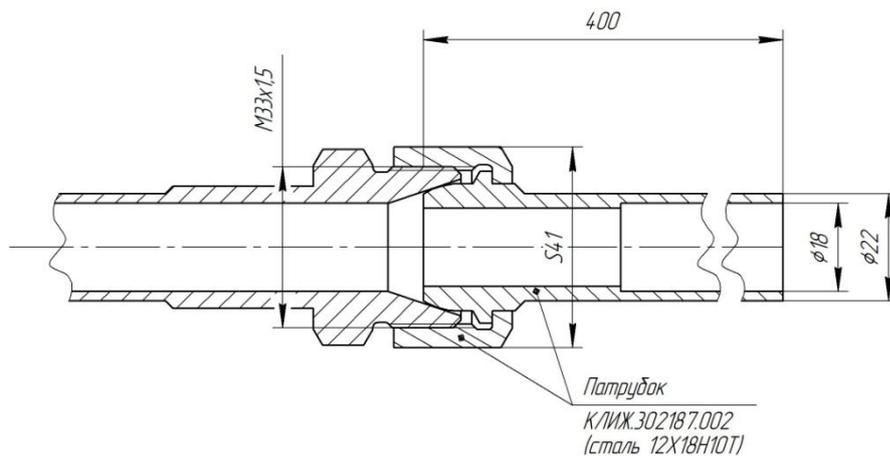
Крепление патрубка КЛИЖ.302187.002 (сталь 12Х18Н10Т)
